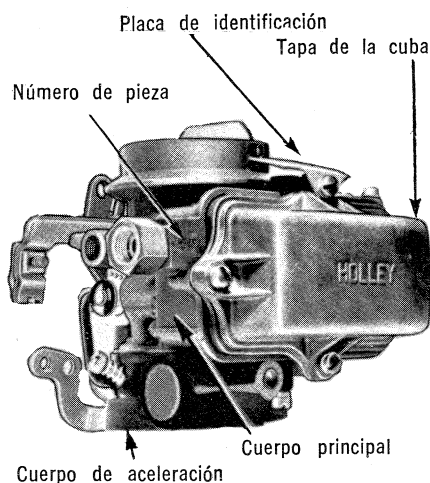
Carburador Holley BA-C9 DZ-9510-B.
